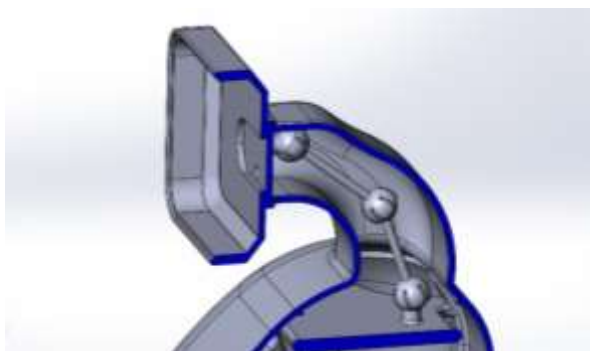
Шарнирный механизм аппарата лазерной эпиляции
